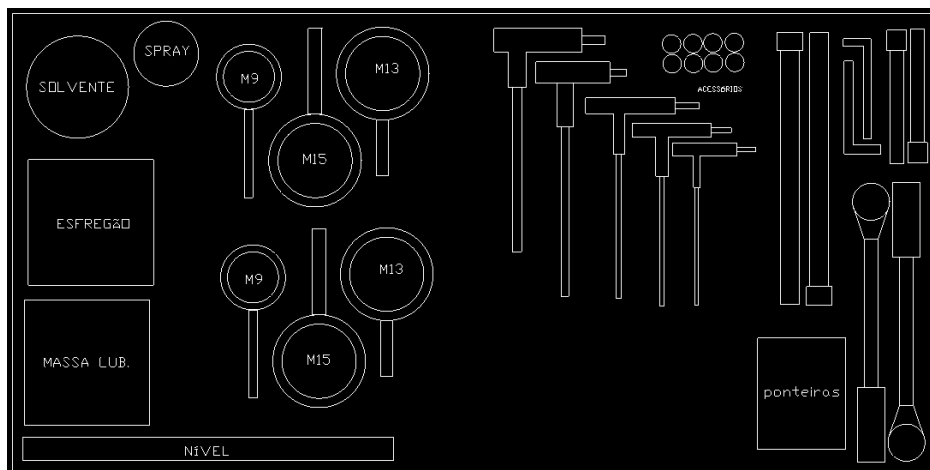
Layout proposto das ferramentas e acessórios do carrinho SMED
